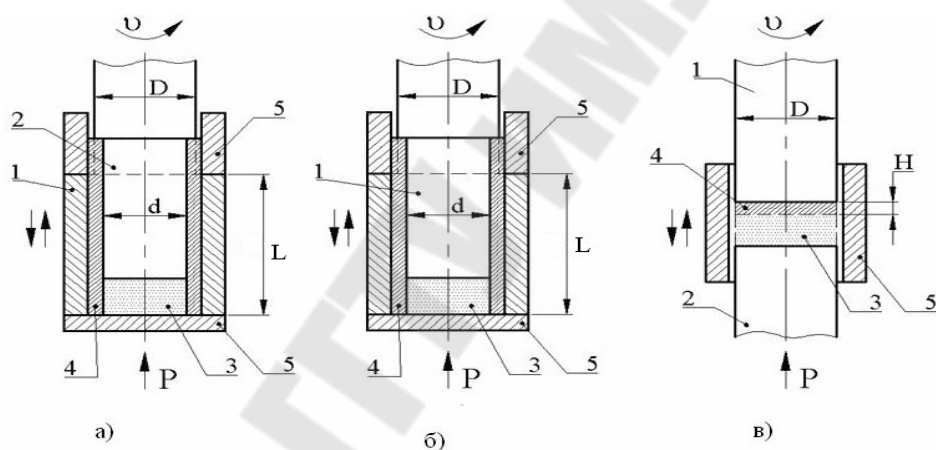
Принципиальные схемы процесса наплавки трением: а – на внутреннюю; б – на наружную; в – на торцовую поверхности; 1 – деталь; 2 – инструмент; 3 – наплавляемый металл до наплавки; 4 – наплавленный металл; 5 – приспособление
